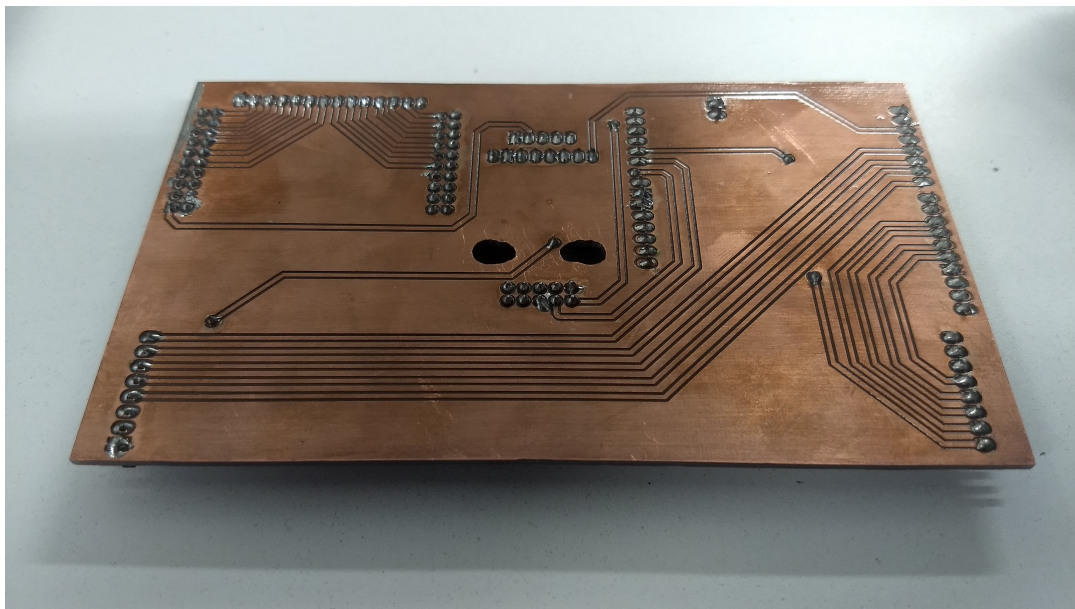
Soldado y acabado del circuito impreso, parte bottom
